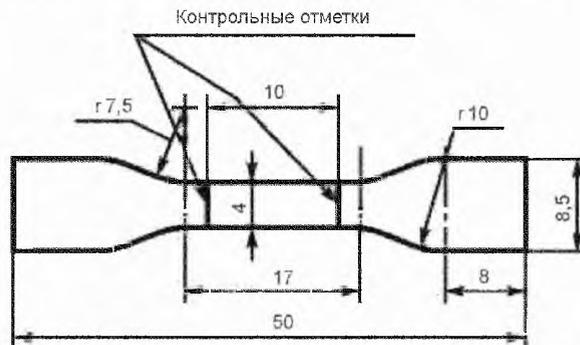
Образец в виде двусторонней лопатки с меньшими размерами
